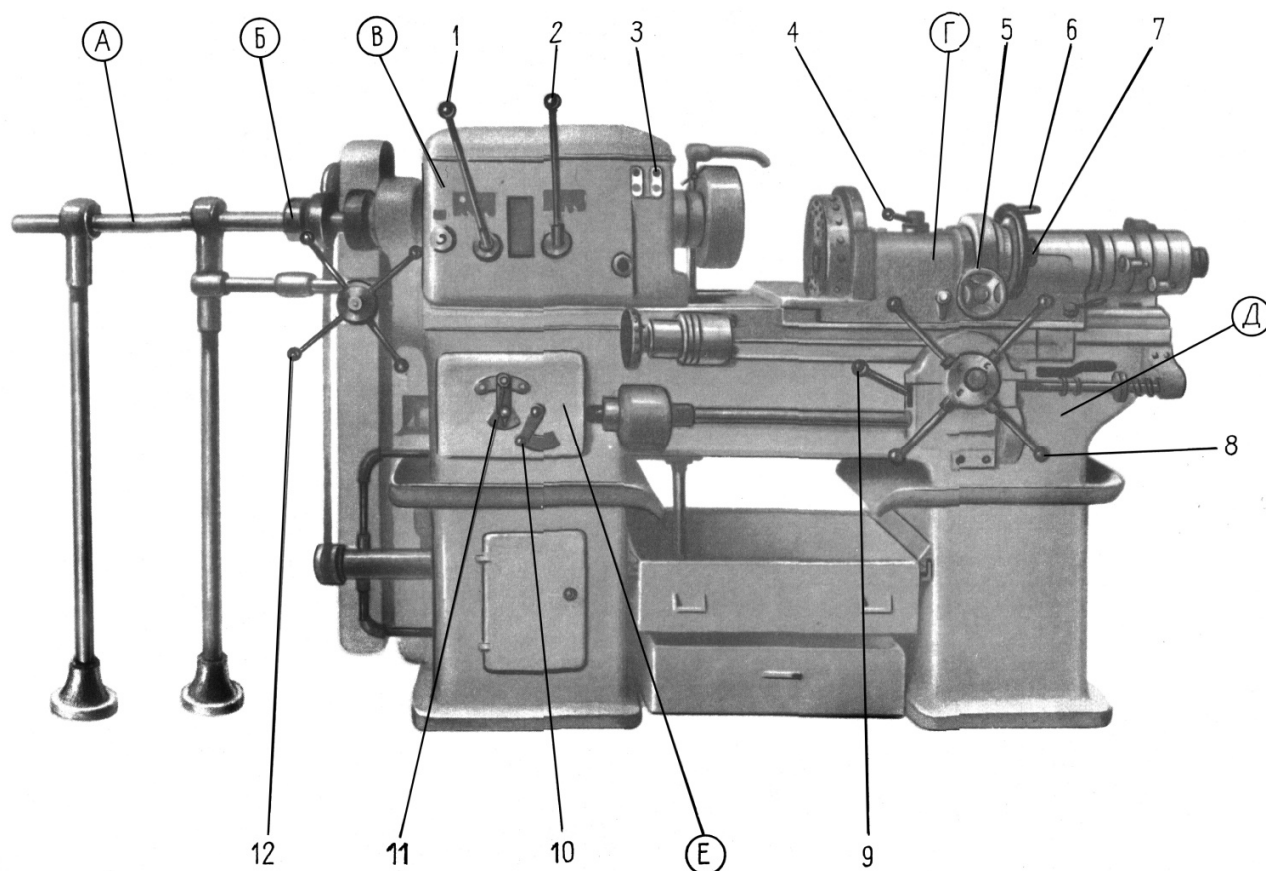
Внешний вид токарно-револьверного станка мод. 1336М
